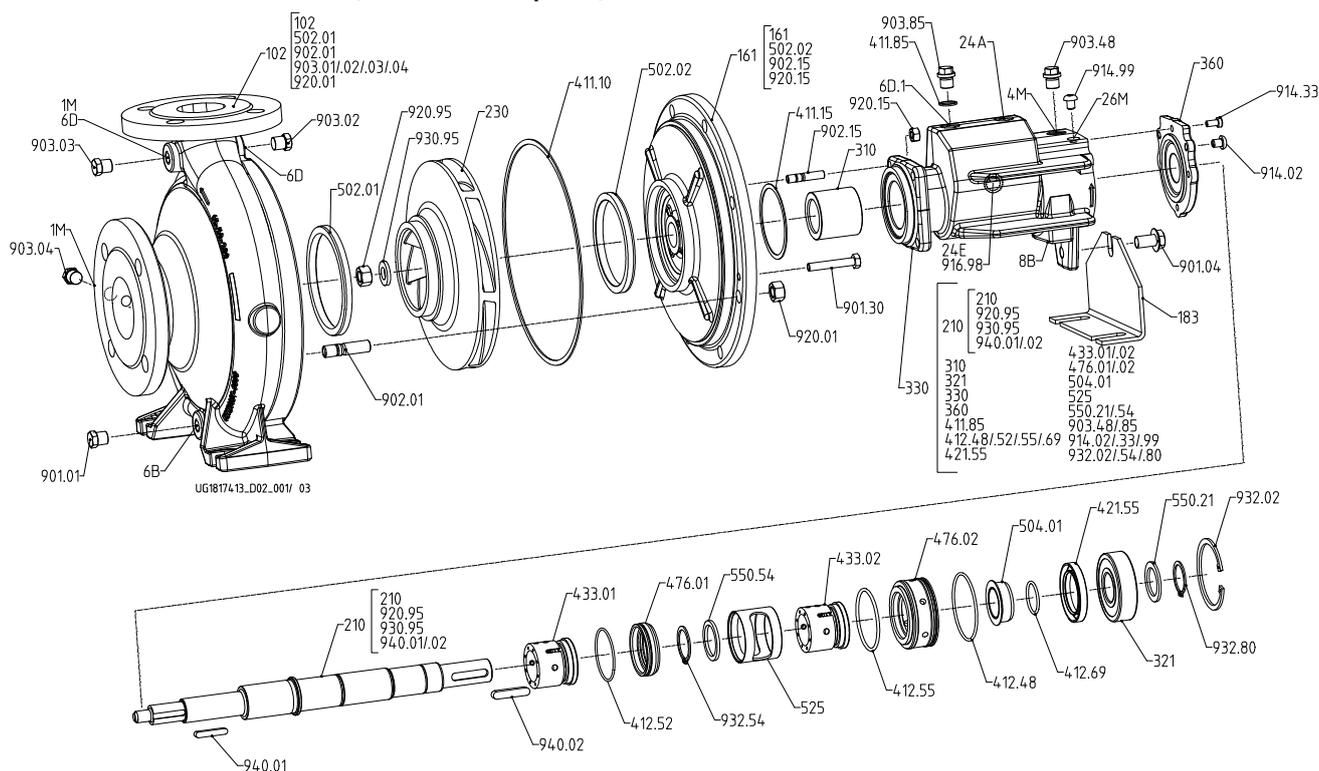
Vista detallada de Etanorm SYT, soporte de cojinetes WS_25_LS con cierre mecánico doble (construcción especial)
